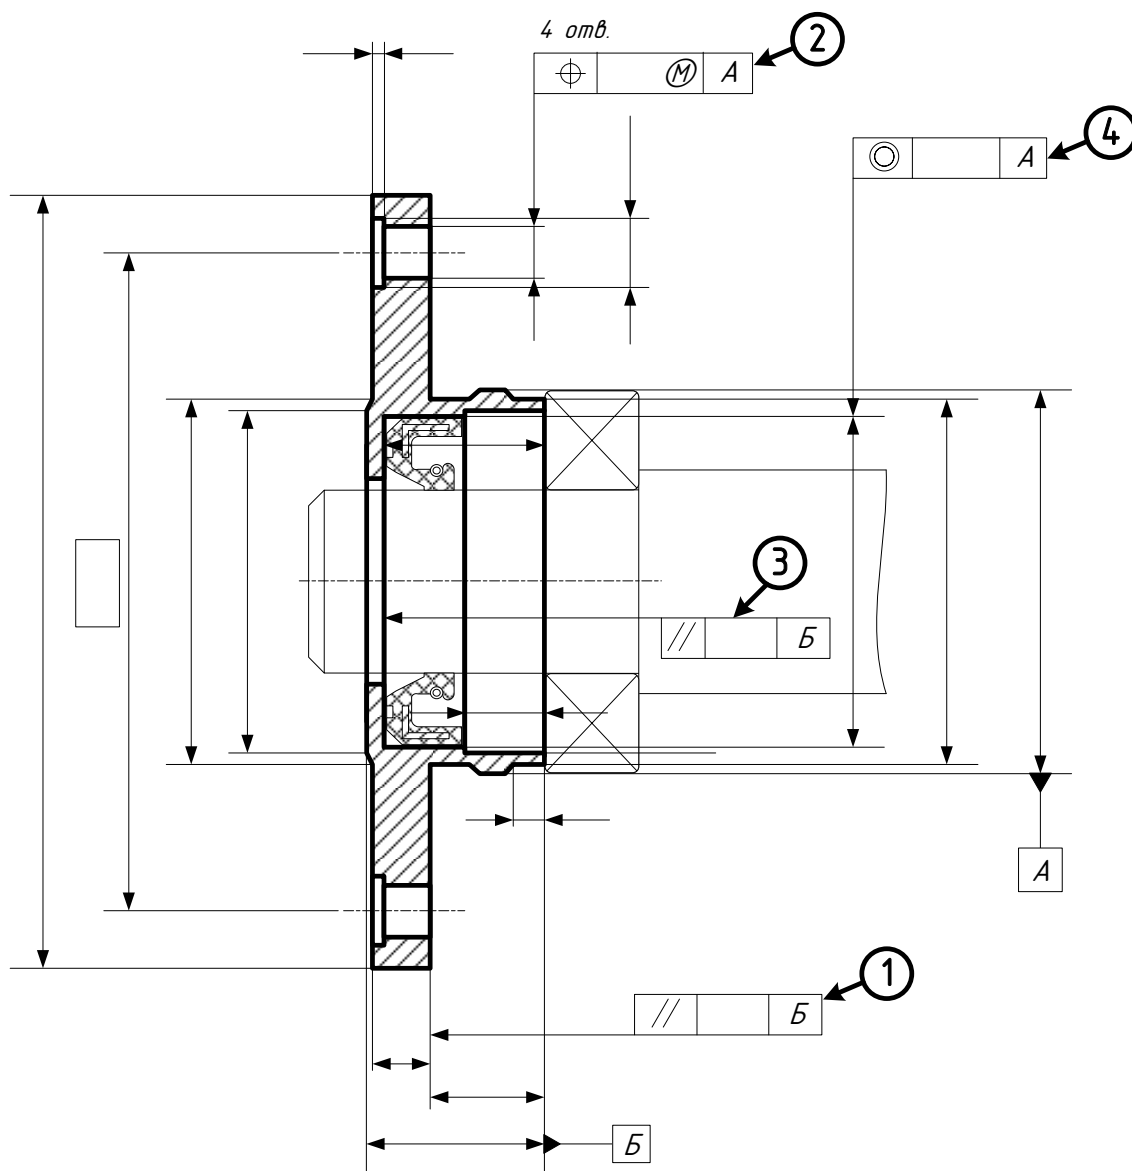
Назначение допусков на крышки подшипников
